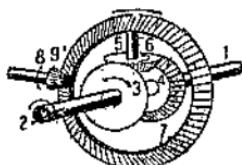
Схема движения ведущих колес автомобиля на повороте.
